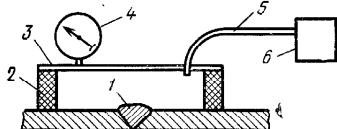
Вакуумная камера для контроля плотности сварных швов:
